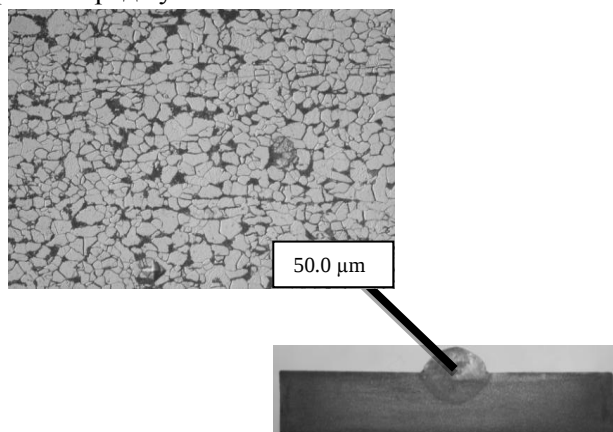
Структура сварного шва. Сварка в среде углекислого газа без применения модификаторов
